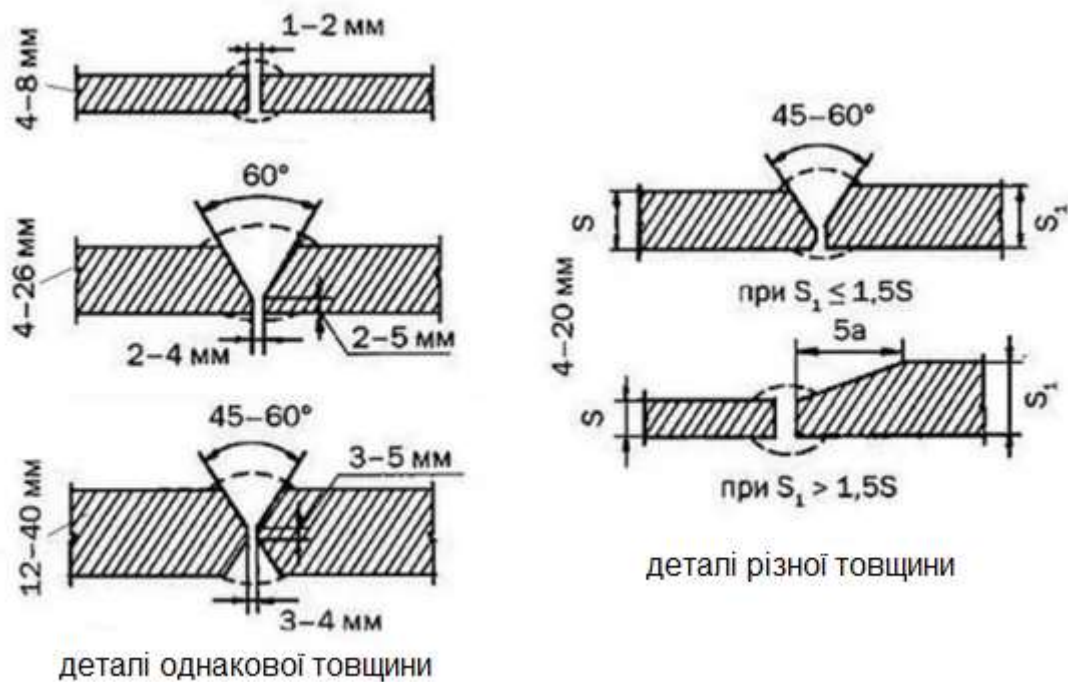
Схеми обробки кромки металу при з'єднанні деталей встик
